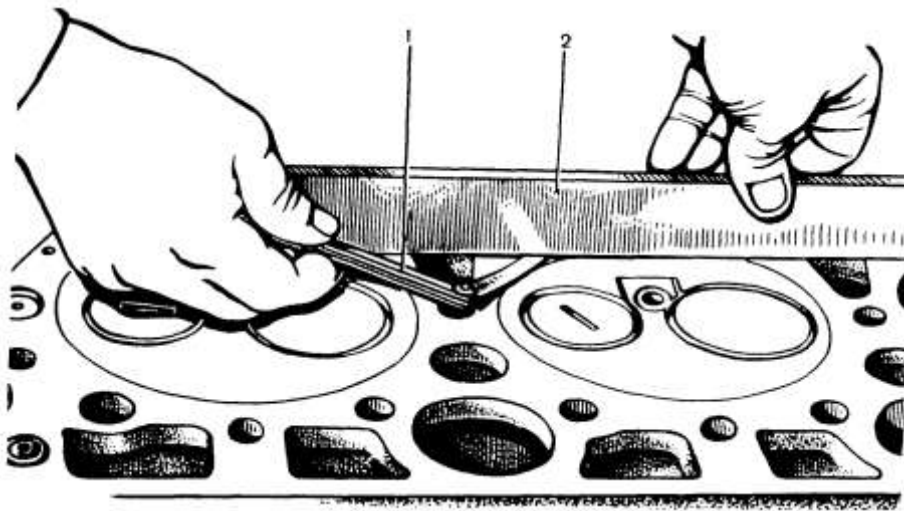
Проверка коробления плоскости головки цилиндров.
